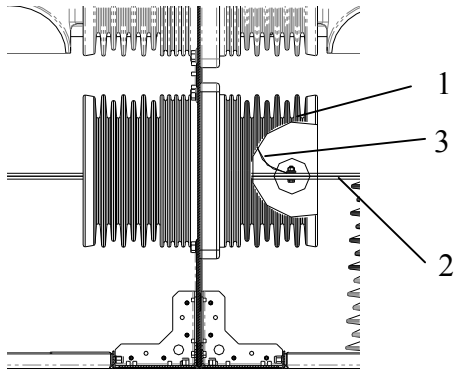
Монтаж сборных шин 1600 А (вид снизу на шкафы КРУ)
